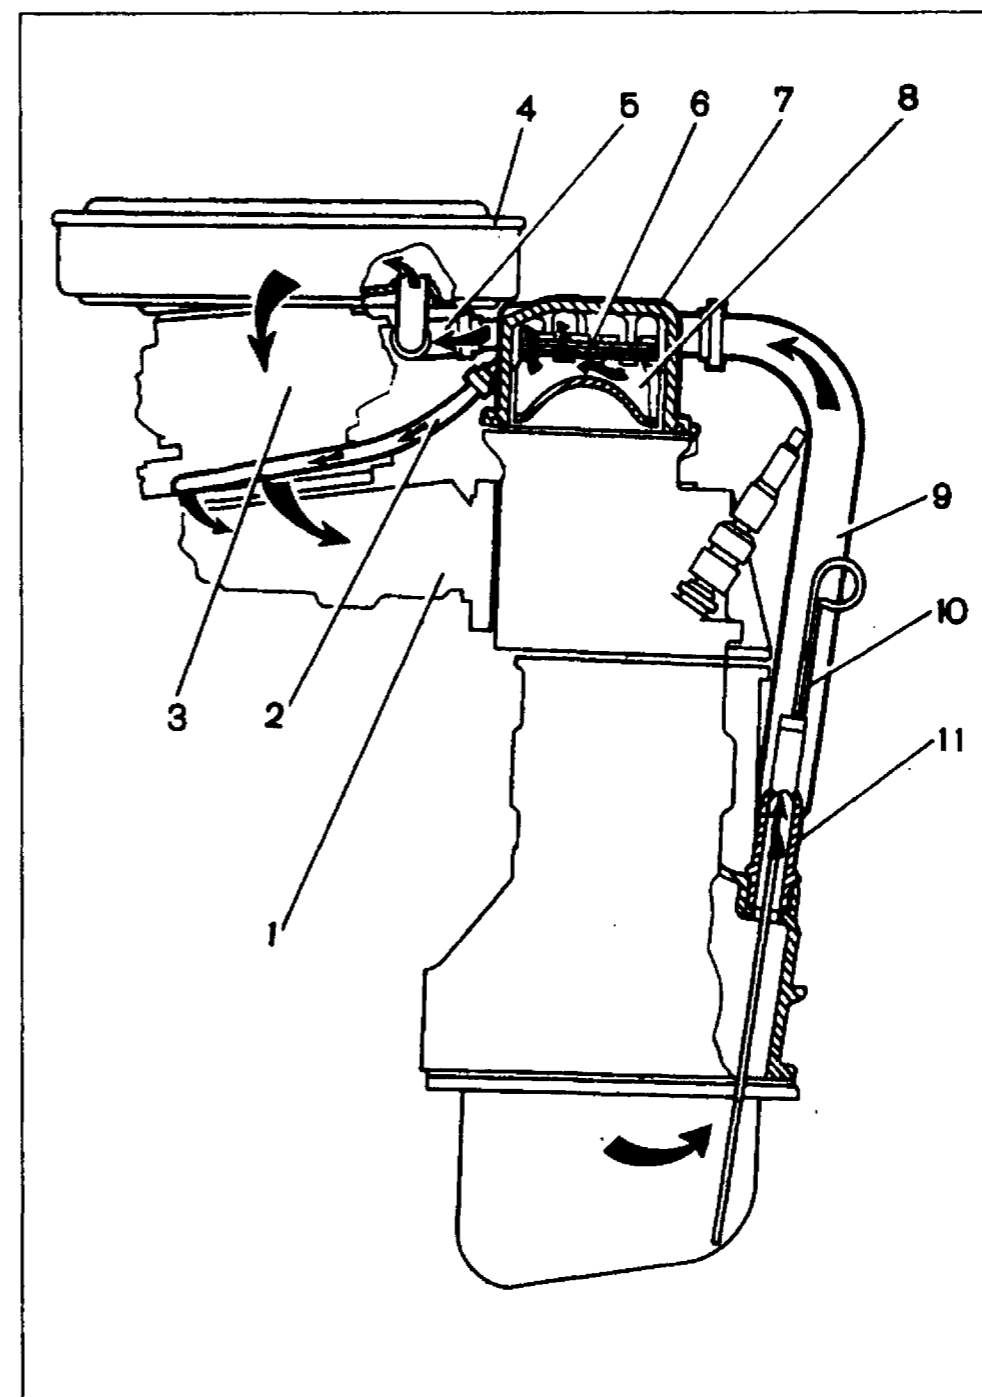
Схема вентиляции картера двигателя: 1 — впускная труба; 2 — шланг отвода картерных газов в задроссельное пространство карбюратора; 3 — карбюратор; 4 — воздушный фильтр; 5 — верхний вытяжной шланг вентиляции картера; 6 — сетка маслоотделителя; 7 — крышка головки блока цилиндров; 8 — корпус маслоотделителя; 9 — нижний вытяжной шланг вентиляции картера; 10 — указатель уровня масла; 11 — штуцер
